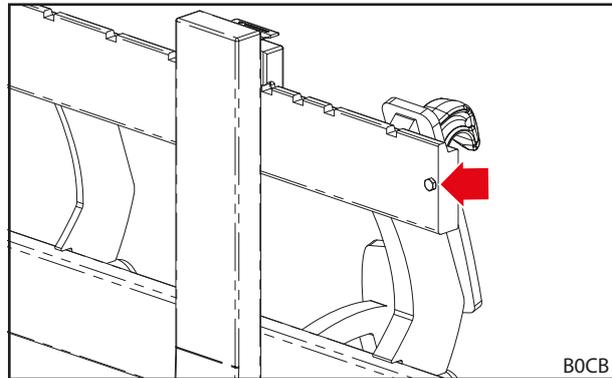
Rimuovere la vite esagonale dall'estremità del profilo
